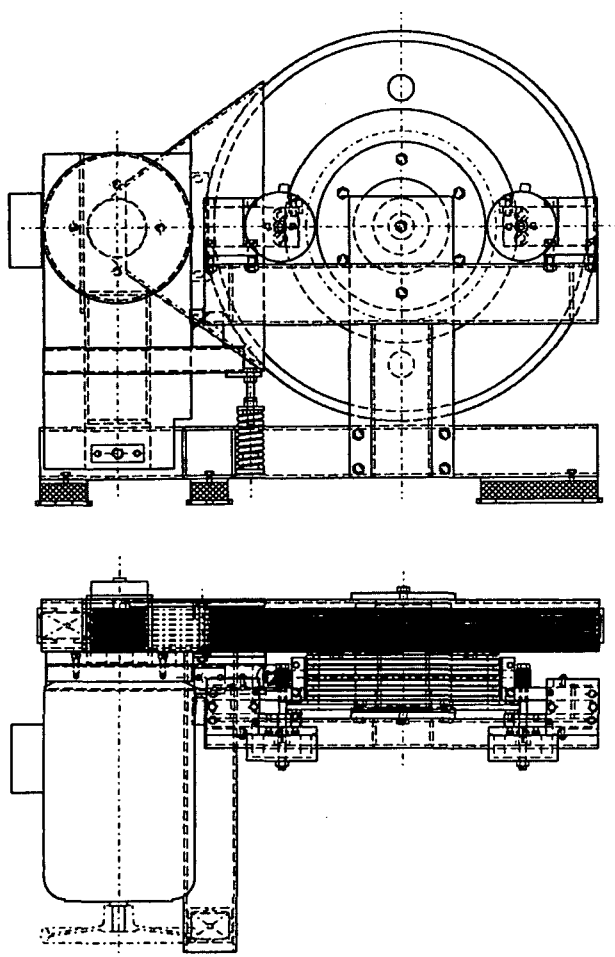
Чертеж лебедки с клиноременным приводом (Ingenieurburo fur Aufzugtechnik)
